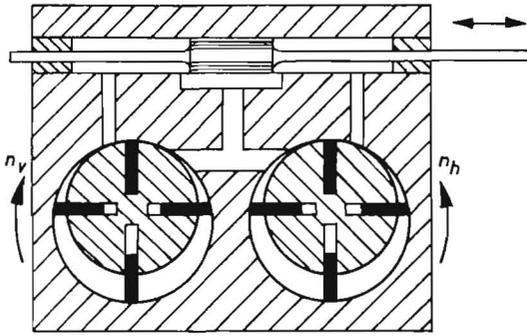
Hydraulischer Schlupfmesser mit mechanischer Übertragung
